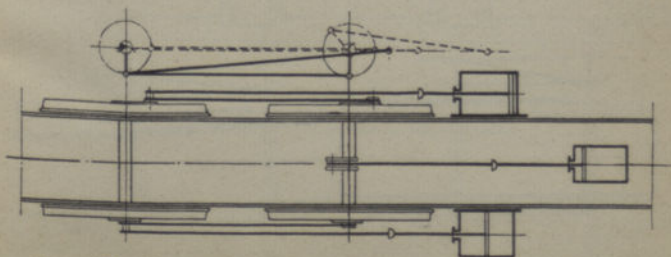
Mechanismo motor de locomotiva compound de 3 cylindros.
